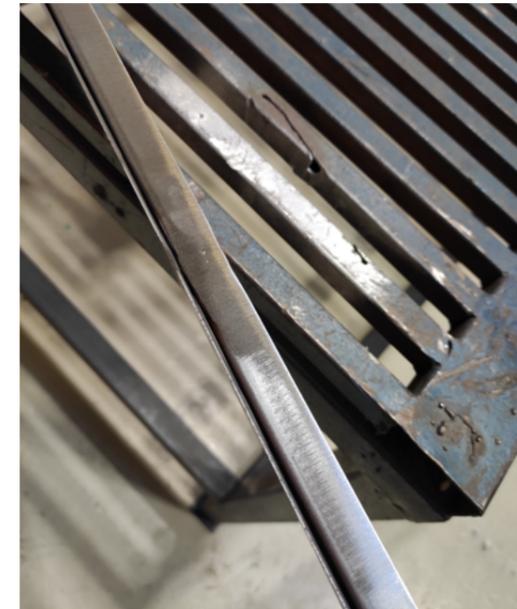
Diego Vidal. Repasado de soldaduras.
